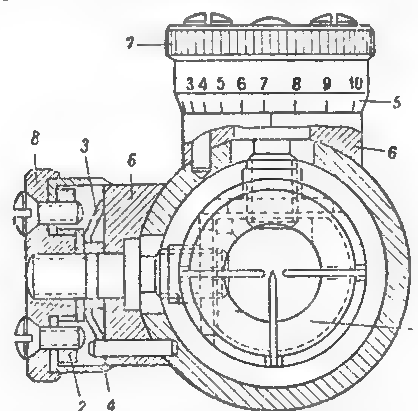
Механизм установки углов прицеливания и боковых поправок:
